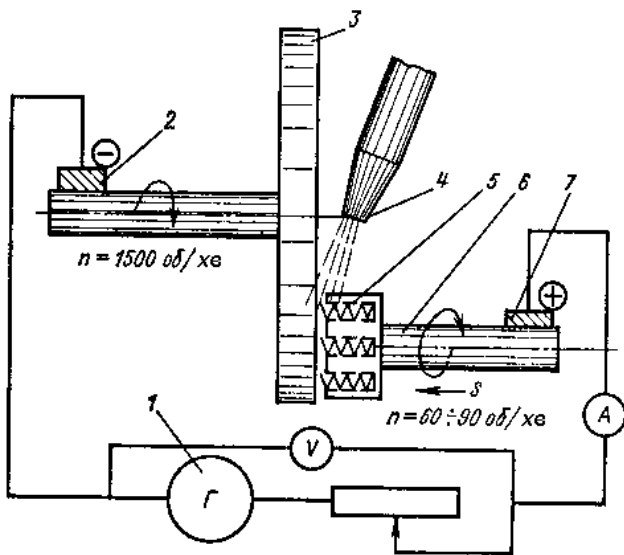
Принципова схема електрохімічного шліфування торцевих поверхонь пружин: 1 – генератор постійного струму; 2, 7 – щітки; 3 – електрод-інструмент (катод); 4 – електроліт; 5 – оброблювана деталь (анод); 6 – пристосування; S – подача виробу.
